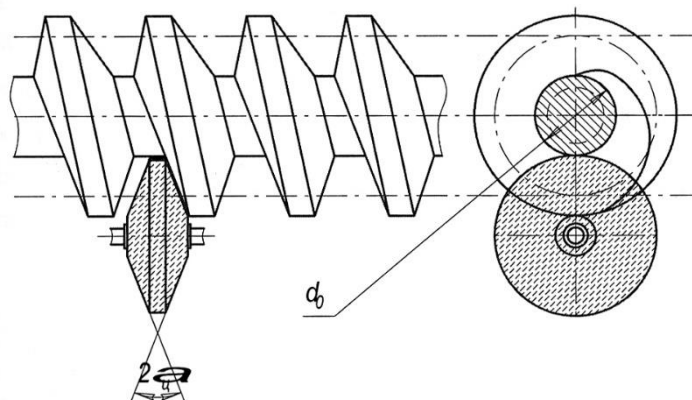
Схема шліфування евольвентного черв'яка однією стороною дискового круга
